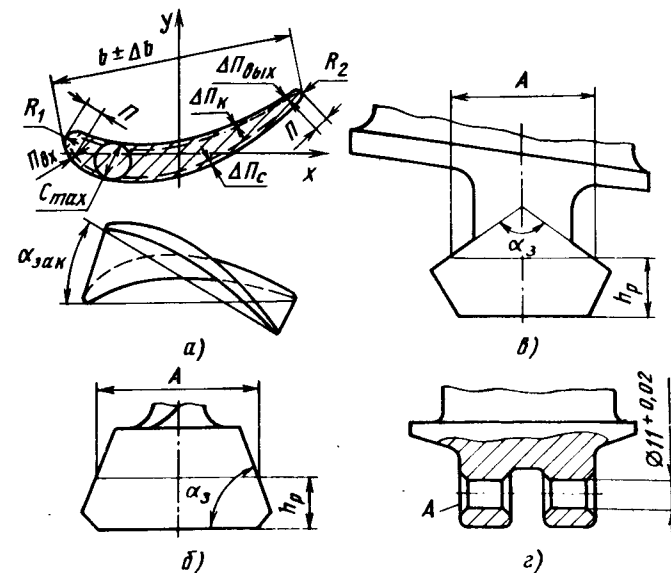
Основные конструктивные элементы рабочих лопаток компрессора, определяющие точность их изготовления:
